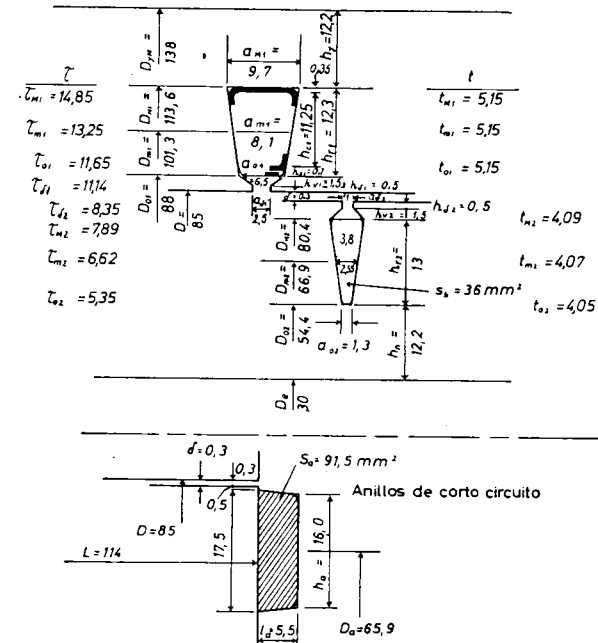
a. Dimensiones de la plancha de un motor de 2CV, 1.500 r/m.
